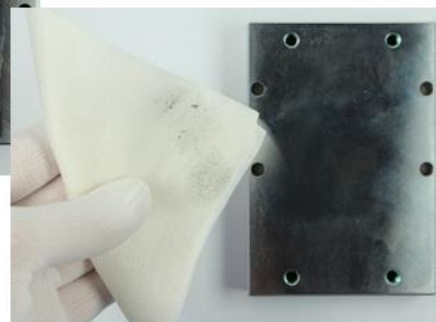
Reinigung der Montagefläche für das Wechseln eines Moduls
